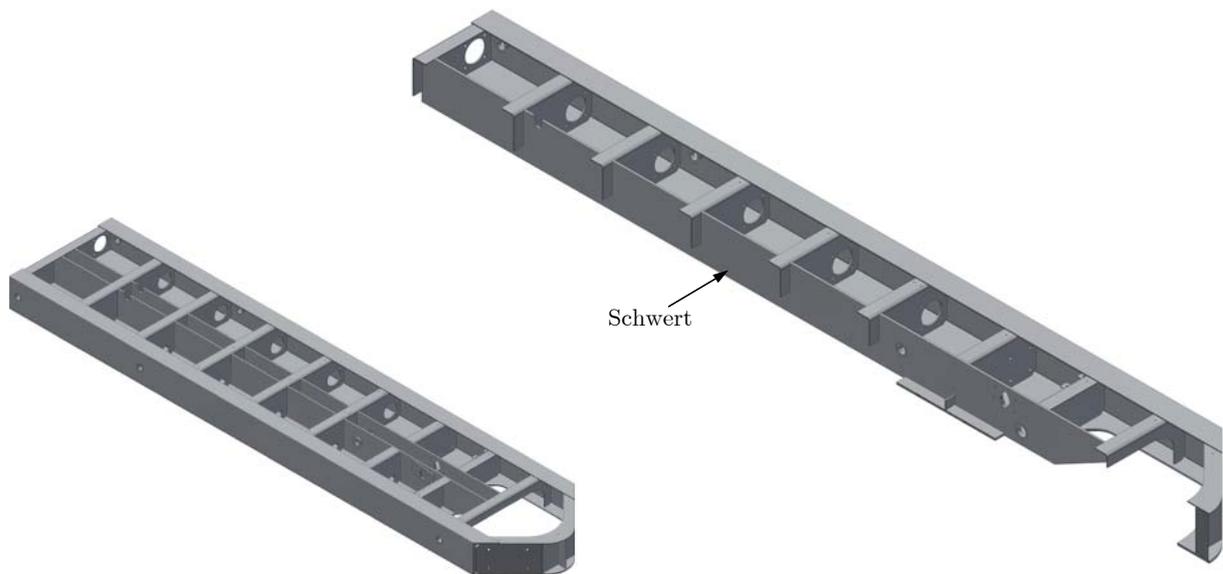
Laden-Schweißbaugruppe (Voll- und Schnittansicht von vorne)
